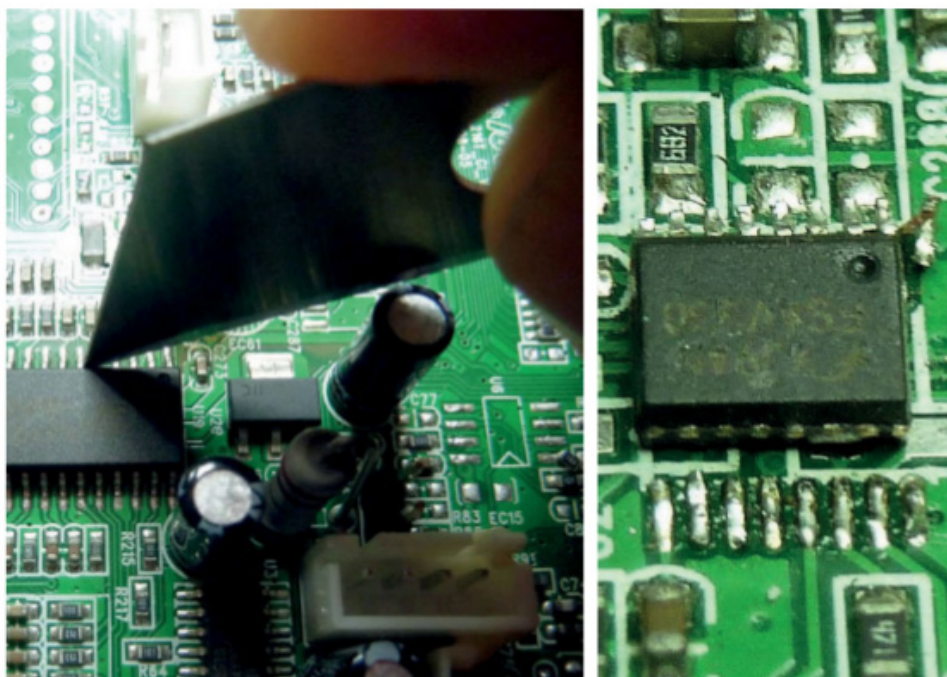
Découpe au cutter des broches de circuits intégrés
